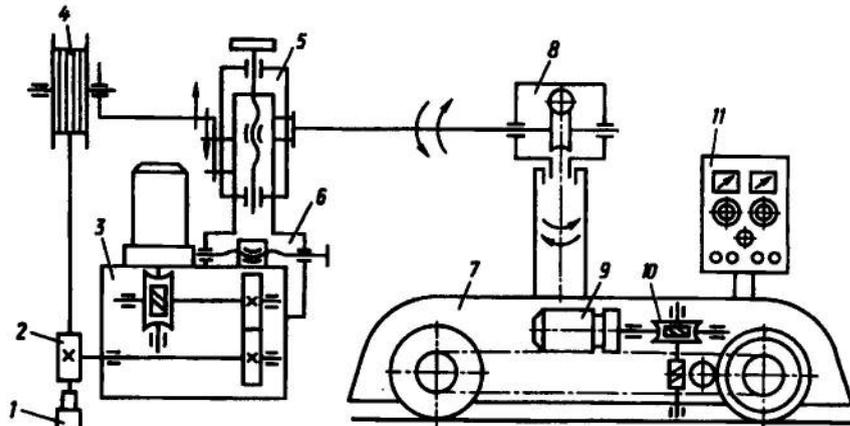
Схема автомата для зварювання плавким електродом:
